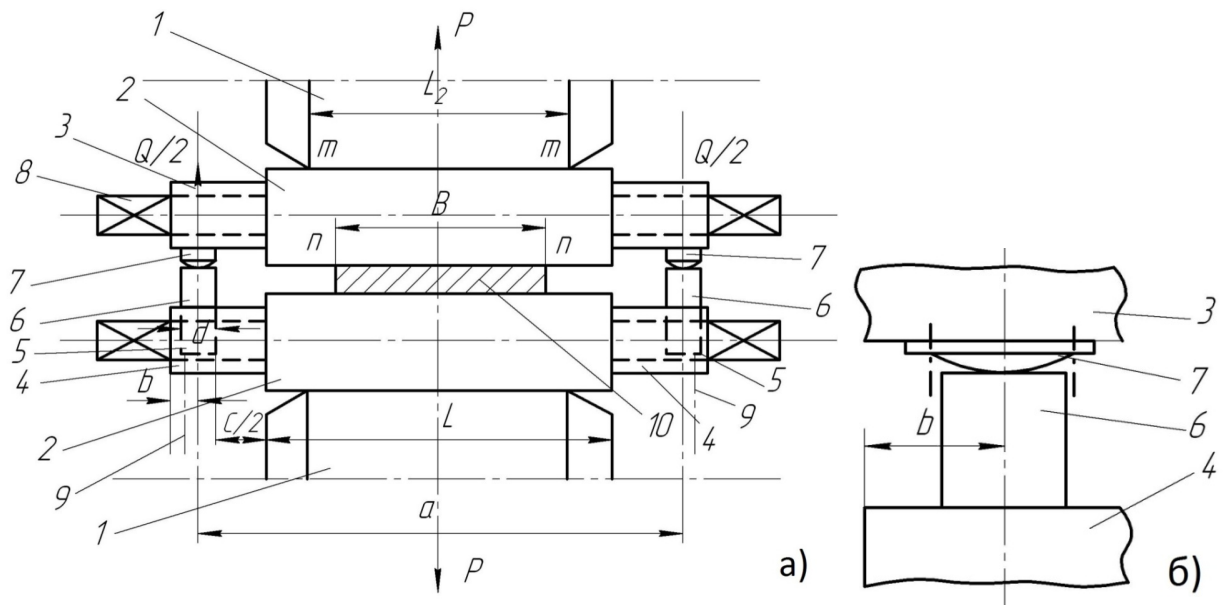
Пристрій для регулювання прогину валка: 1 - опорні валки; 2 - робочі валки; 3 - подушки верхніх робочих валків; 4 - подушки нижніх робочих валків; 5 - гідроциліндри; 6 - плунжера; 7 - прокладка зі сферичною опорною поверхнею; 8 - хвостовікі приводів; 9 - гідросистема харчування гідроциліндрів.
